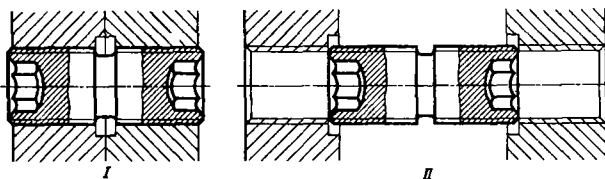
Соединение деталей болтом с резьбой противоположного направления: I и II — положения после и перед сборкой
